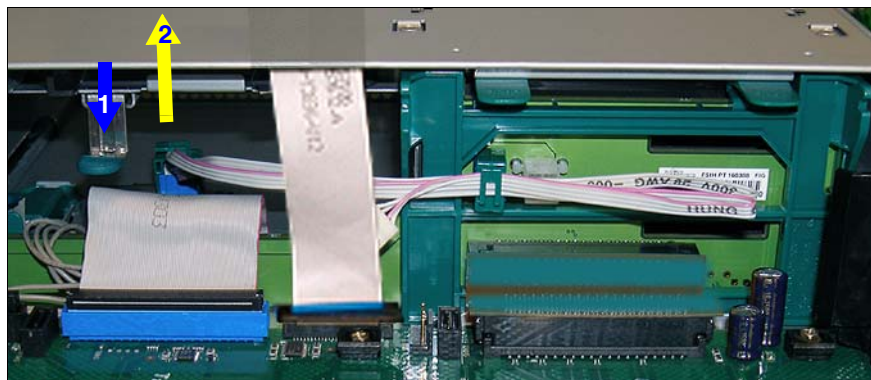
Entriegeln FD-Laufwerksmodul (zur besseren Sicht wurde die Lüfterbox entfernt)
